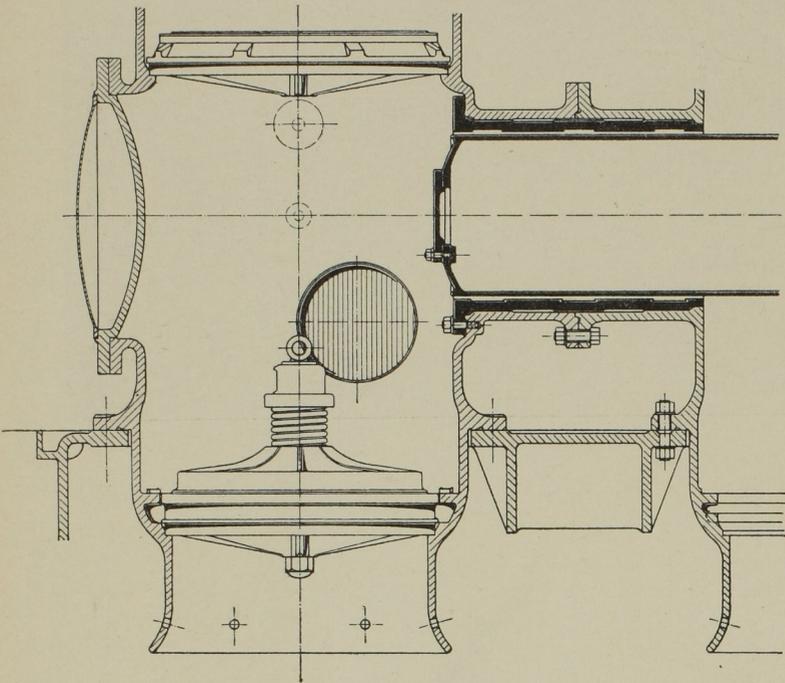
Pumpenkolben und Ventil. Masst. 1:20.
